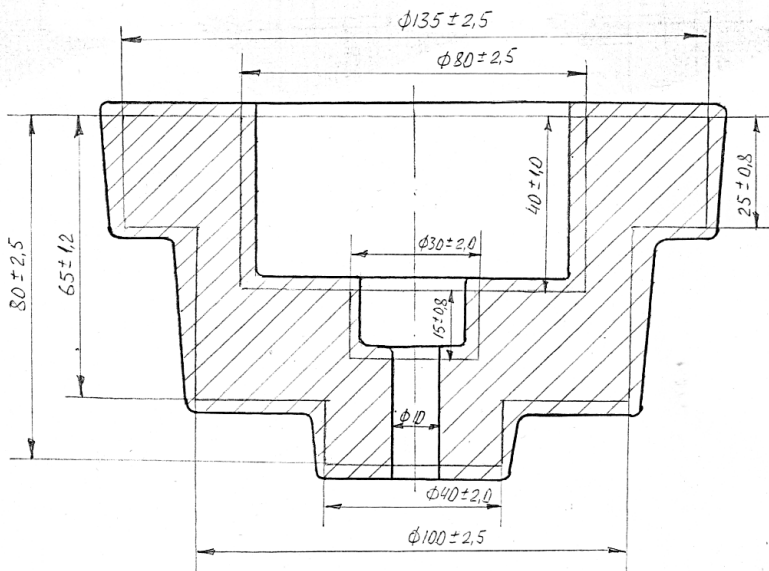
Чертеж отливки с учетом допусков на литьё
